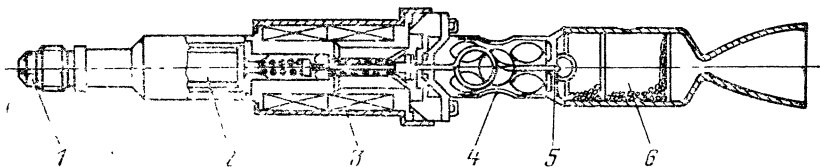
Конструктивная схема гидразинового двигателя:
